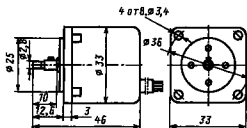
39 Габаритные и установочные размеры двигателя ДШИ-1М
